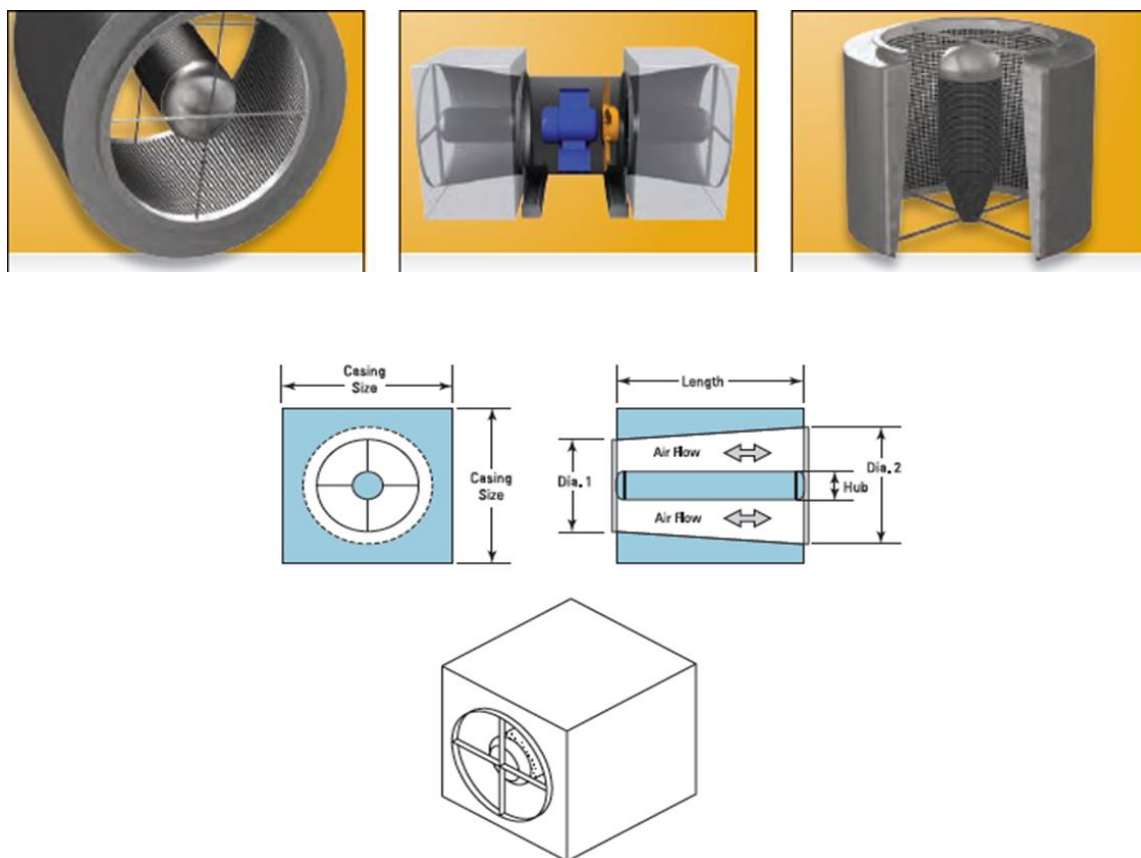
Глушитель с цилиндрической вставкой и прямоугольной формой наружного корпуса серии AFS производства фирмы Price.
